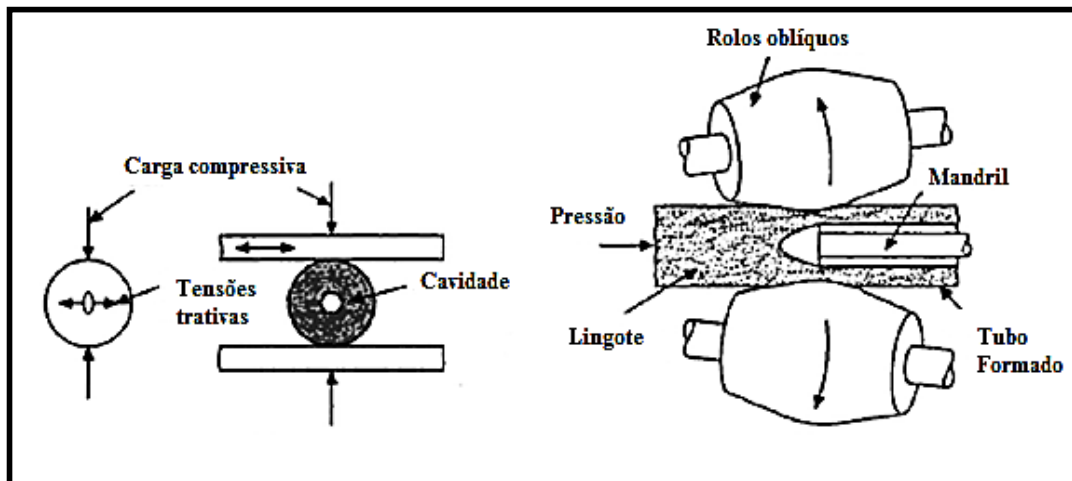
Ilustração do esquema do laminador perfurador, mostrando o posicionamento oblíquo dos rolos laminadores e a passagem do mandril abrindo a cavidade. Adaptado de [20].
